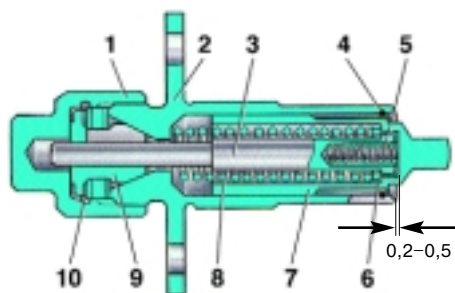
Разрез натяжителя цепи двигателя мод. 2106–70: 1 – колпачковая гайка; 2 – корпус натяжителя; 3 – стержень; 4 – пружинное кольцо; 5 – пружина плунжера; 6 – шайба; 7 – плунжер; 8 – пружина; 9 – сухарь; 10 – пружинное кольцо
